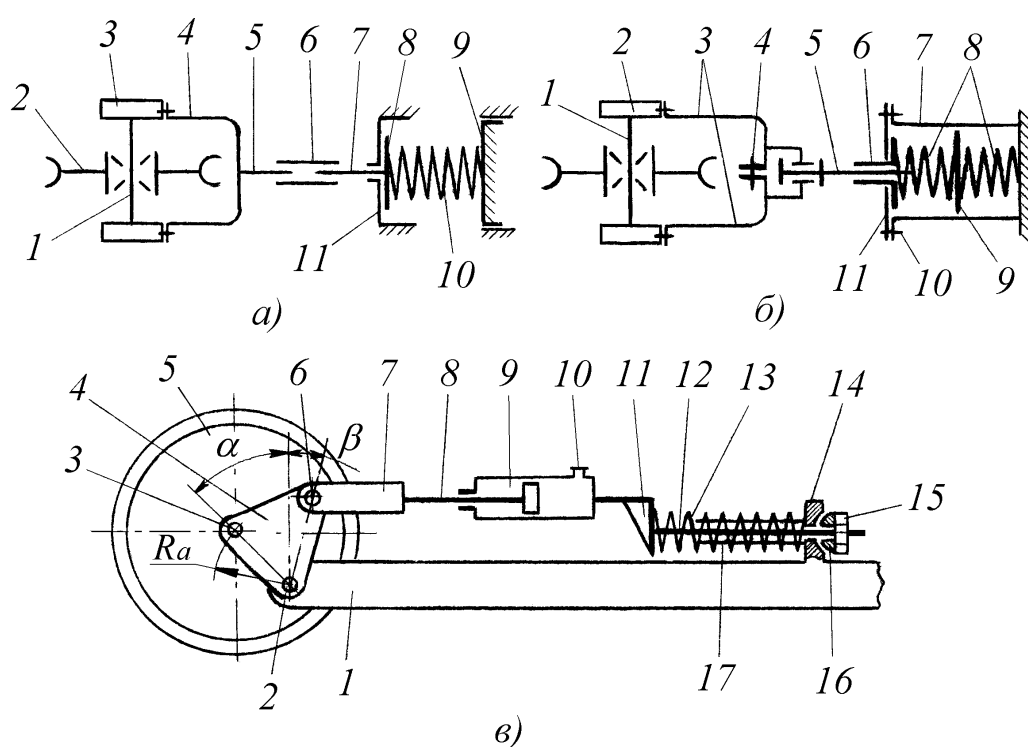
Принципиальные схемы конструкций натяжного и амортизирующего устройств, устанавливаемых на тележке гусениц
